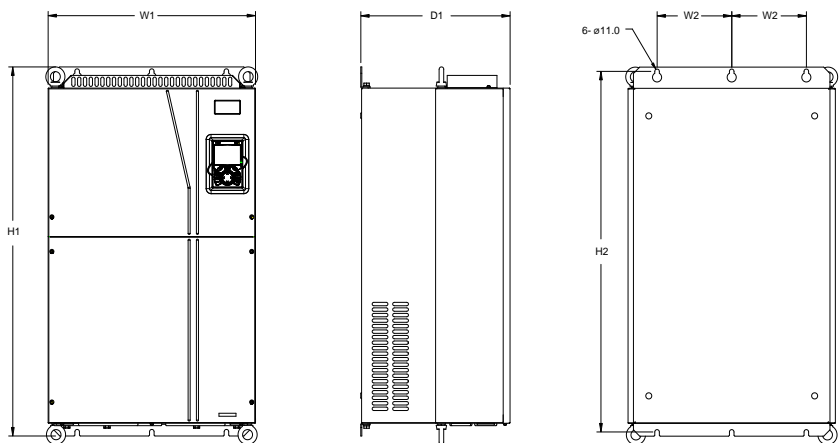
Схема настенного монтажа ПЧ 660 В, от 160 до 220 кВт
